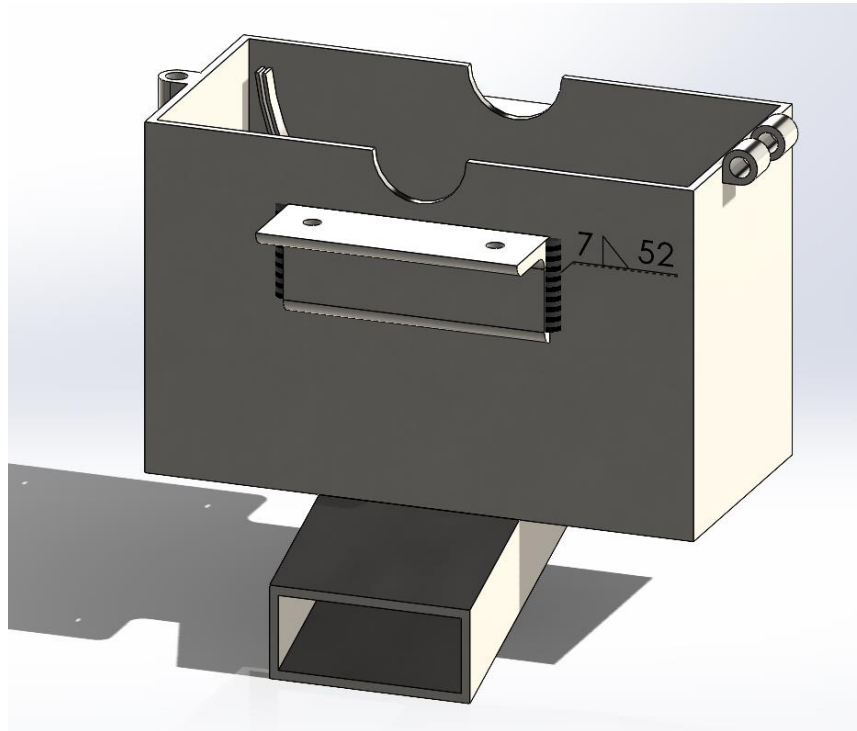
Soldadura TIG simulada en el software SolidWorks.
